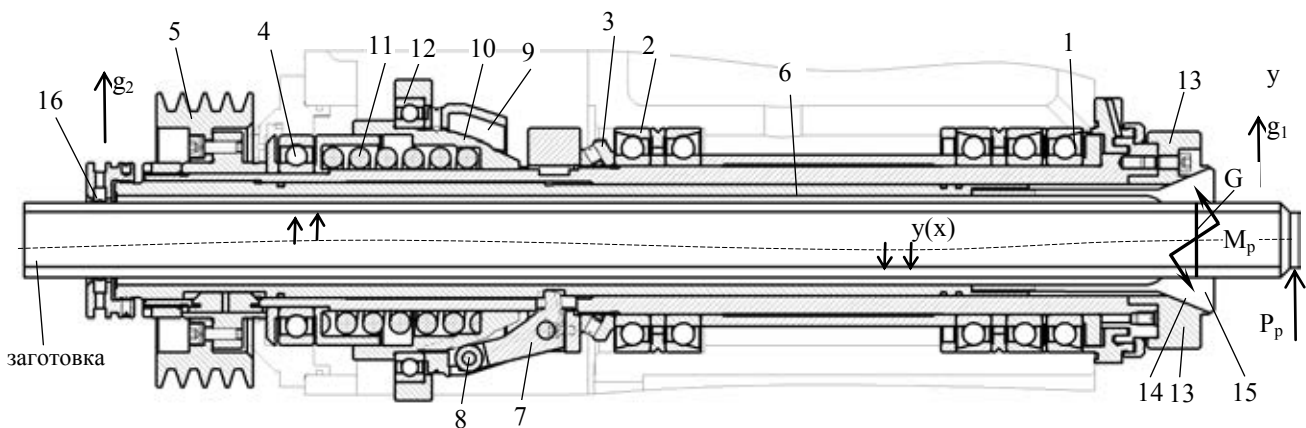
Шпindelний вузол модуля комплексу ТАК із встановленою в патроні заготовкою.
